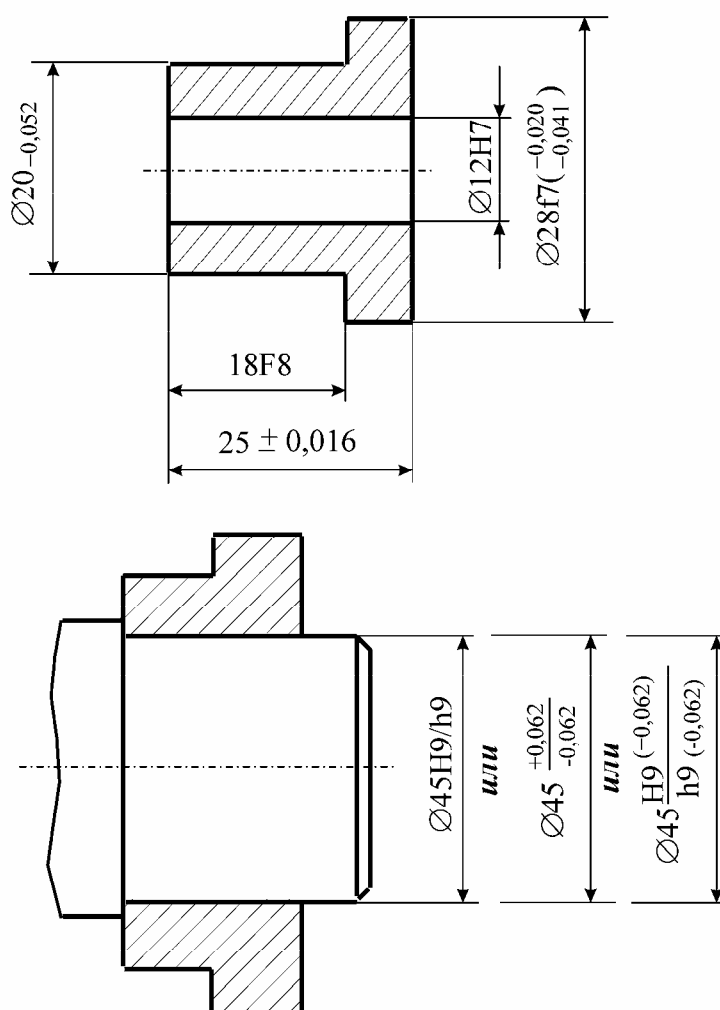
Примеры обозначений полей допусков и посадок на чертежах
